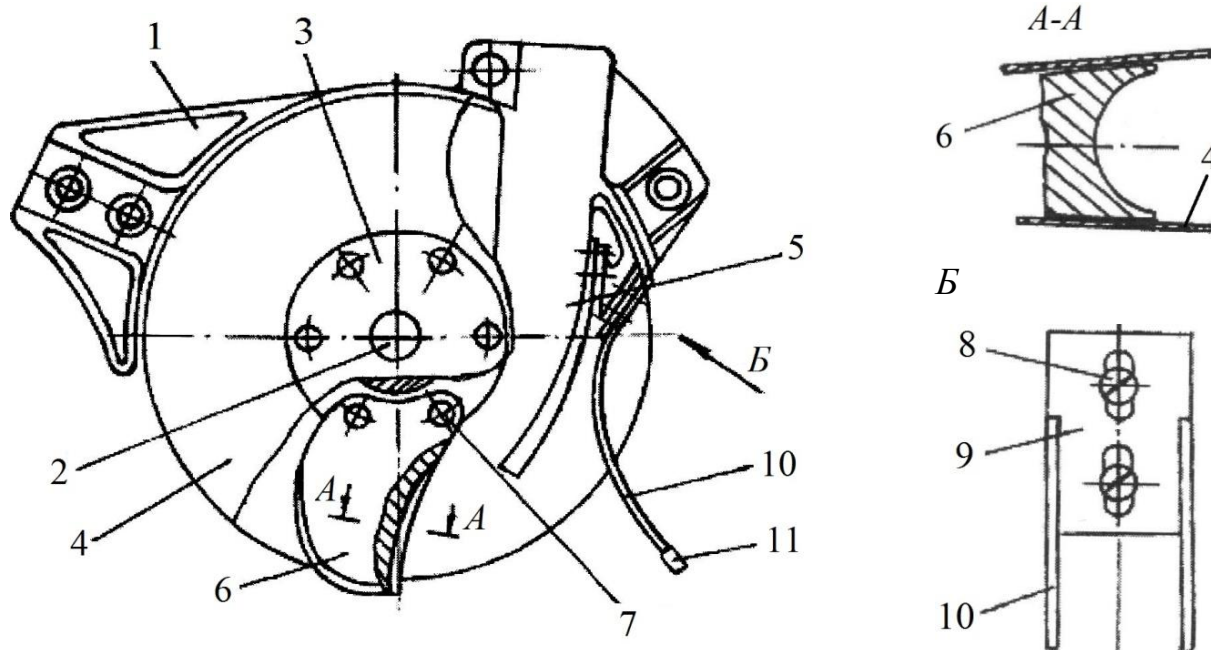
Дводисковий сошник: 1 – корпус; 2 – вісь; 3 – маточина; 4 – диск; 5 – лійка; 6 – п'ята; 7 – заклепки; 8 – гвинти; 9 – пластина; 10 – прутки-загортачі; 11 – кінцівки прутків
